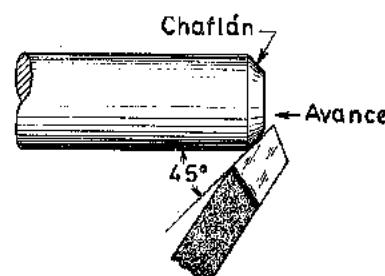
Achaflanado con la cuchilla ajustada a un ángulo.
